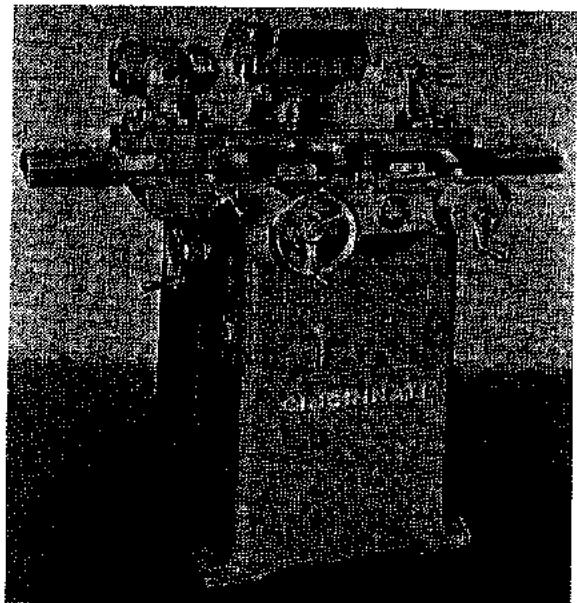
Rectificadora de fresas y herramientas (Cincinnati Milling Machine Co.)
